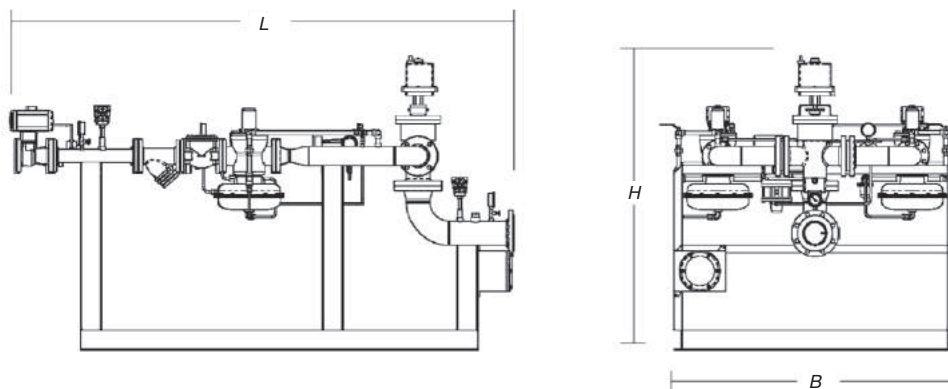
Габаритные размеры смесительной установки Metan-3-2-6800(-55000)-СК
